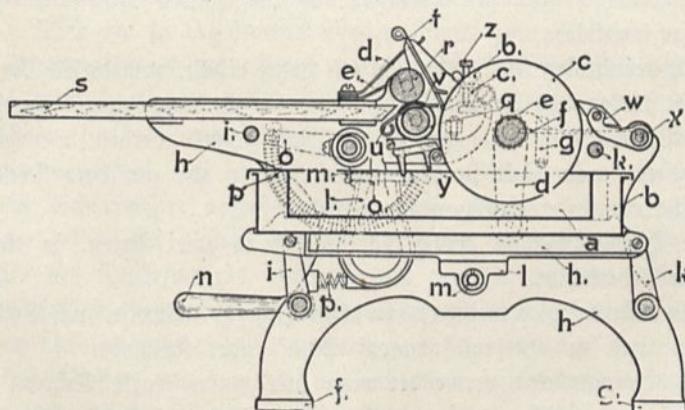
Querschnitt der Anleimmaschine „Prisma“.
